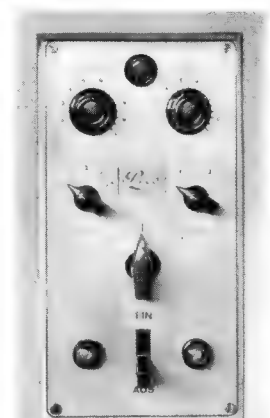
Frontplatte des Steuergerätes der neuen Peco-Punktschweißmaschine
